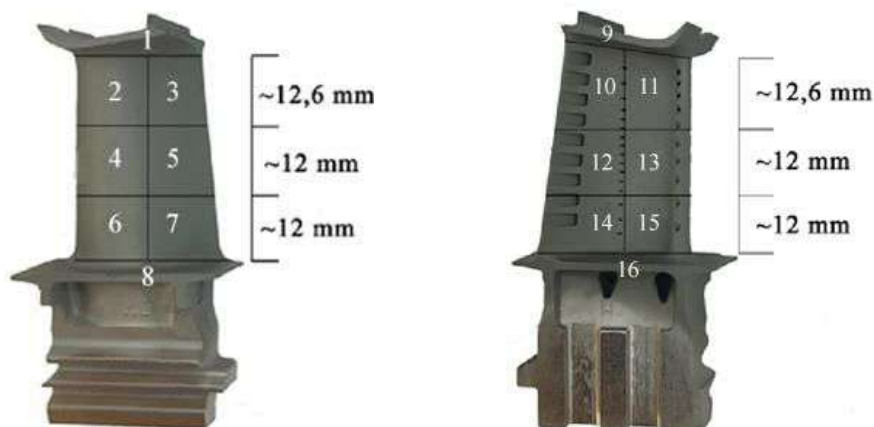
Робоча лопатка з типовою розміткою на зони
